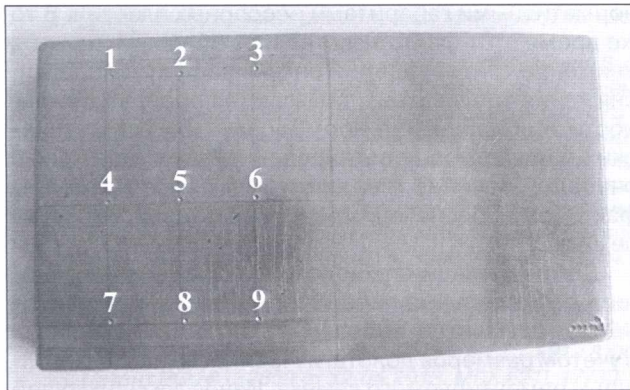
Схема нанесения отпечатков на образцы рессорных листов.
